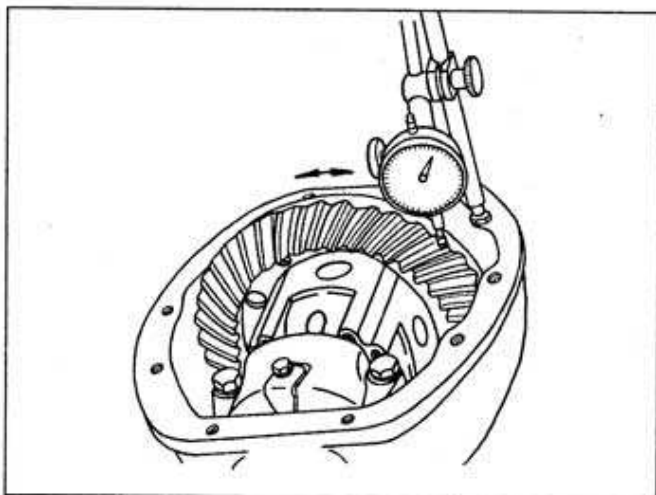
Проверка бокового зазора в зацеплении зубьев шестерен главной передачи (неразъемный задний мост)
